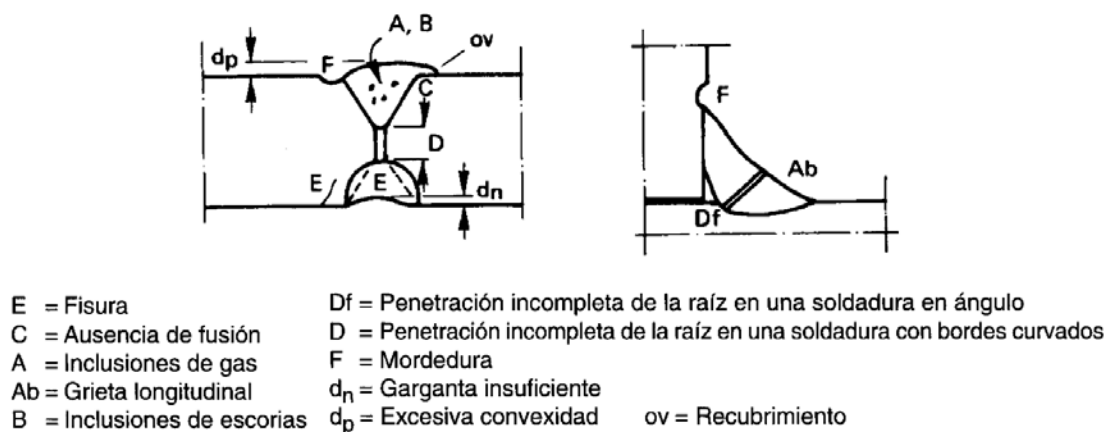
Principales defectos de soldaduras [3]
